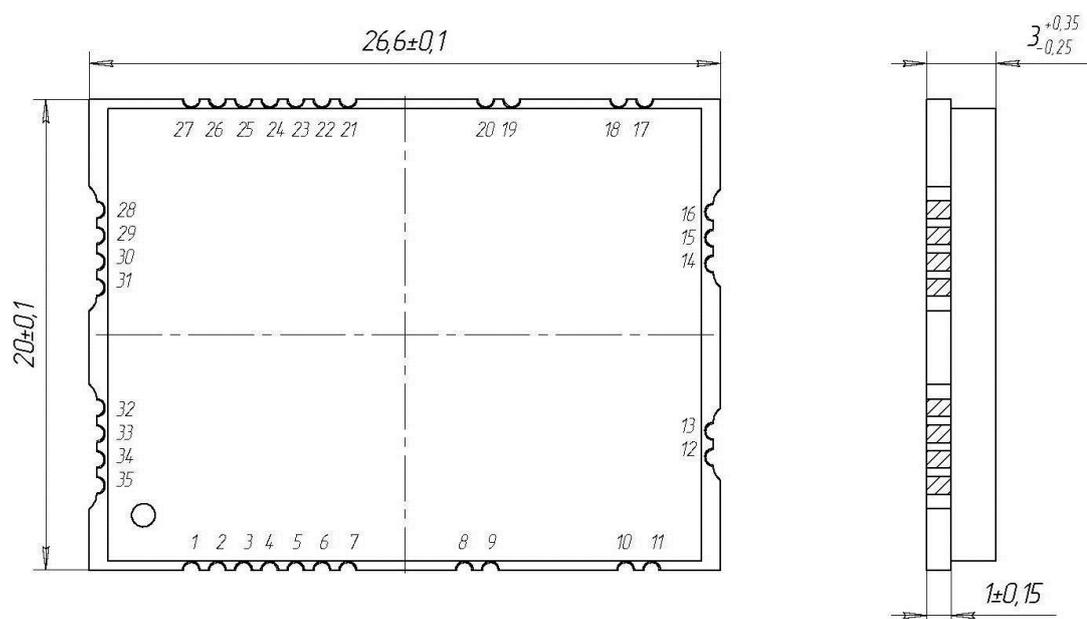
Габаритный чертеж и размеры модуля (размеры указаны в мм)
